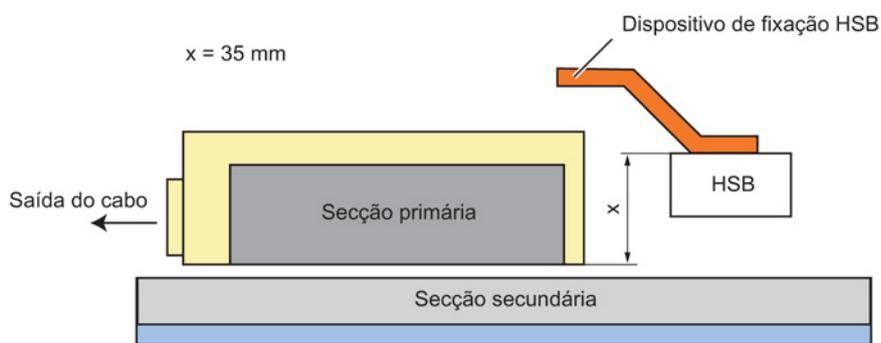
Medida nominal para a montagem da caixa do sensor Hall (HSB)
